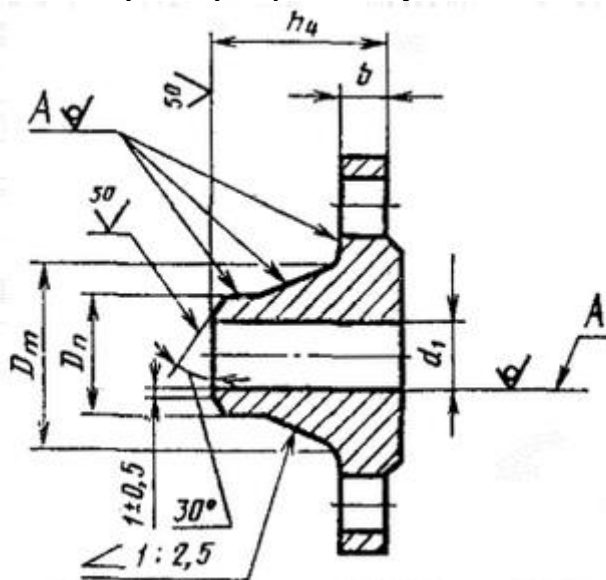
Фланец арматуры, соединительных частей и трубопроводов
